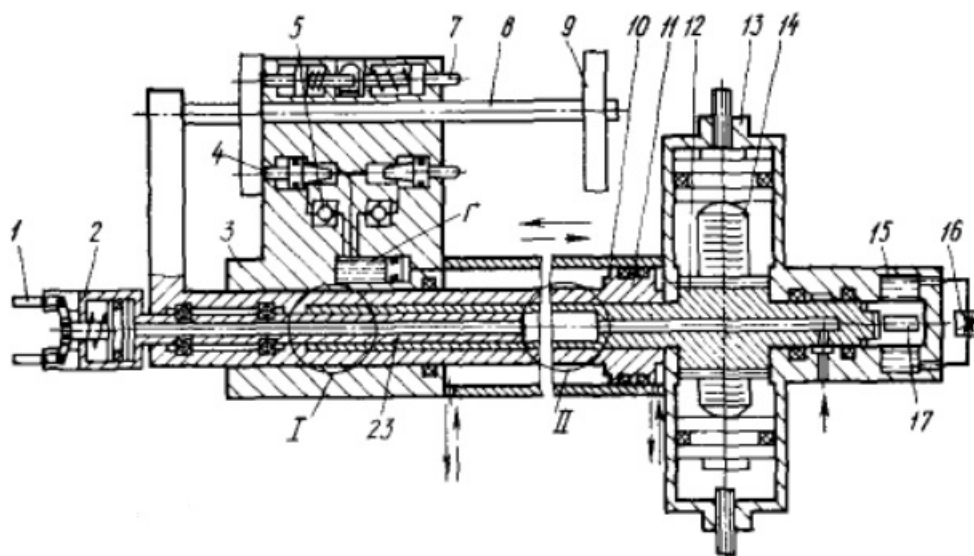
Схема руки маніпулятора «Циклон-3Б»: 1 - захват; 2 – привід затиску захвату; 3 – тормозний пристрій; 4,7 - золотник; 8 – направляюча; 9 – опора; 10 – пневмоциліндр; 11 – шток-поршень; 12 – вал-зубчасте колесо; 13 – привід повороту захвату; 14 – реєчно-зубчаста передача; 15 – гідродемпфер; 23 – валик.[1]
